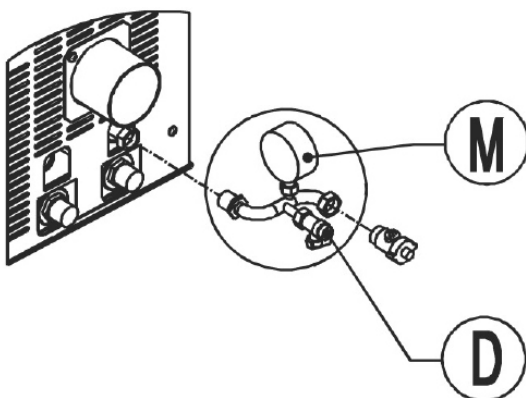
Terminale con rubinetto di caricamento (D) e manometro (M) (Accessorio)
